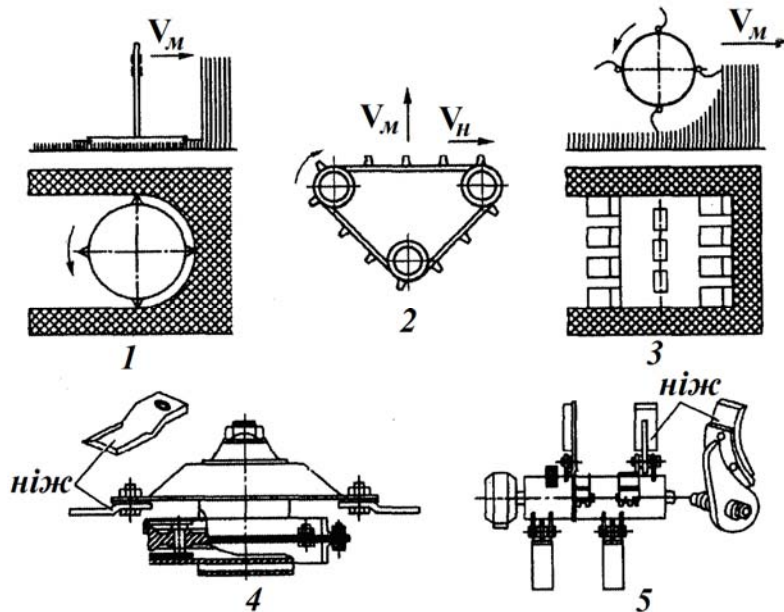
Типи ротаційних різальних апаратів для заготівлі кормів для тваринництва: 1 – з вертикальною віссю обертання ротора; 2 – з прямолінійно-поступальним рухом ножів; 3 – з горизонтальною віссю обертання ротора; 4 – ротор з ножами косарки КРН-2,1; 5 – ротор з ножами косарки для заготівлі подрібненого зеленого корму з кореня.
